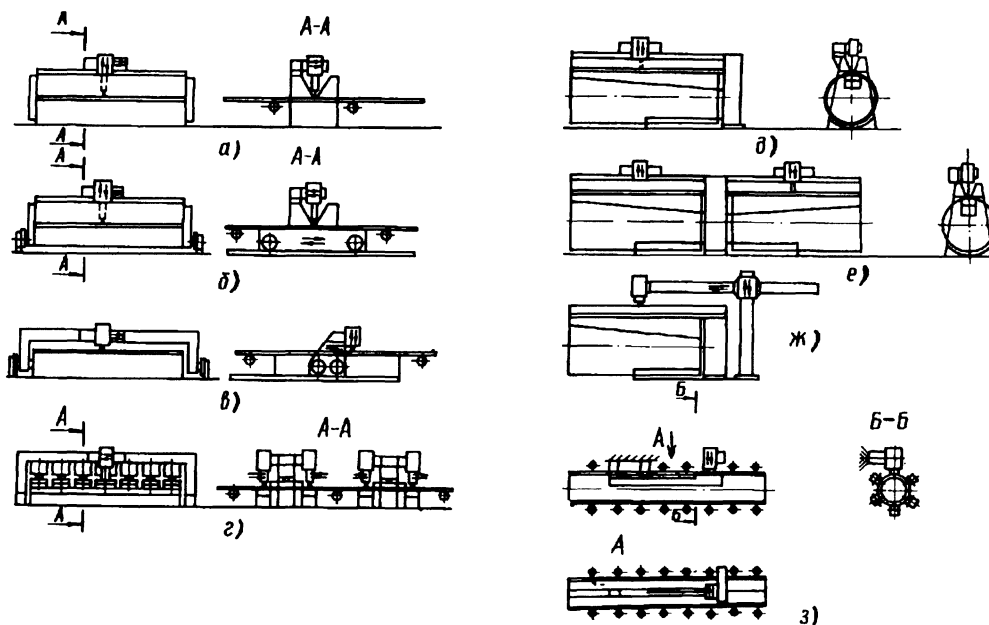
Типовые схемы компоновки установок и станков для дуговой сварки прямых стыковых швов с прижимом свариваемых кромок
